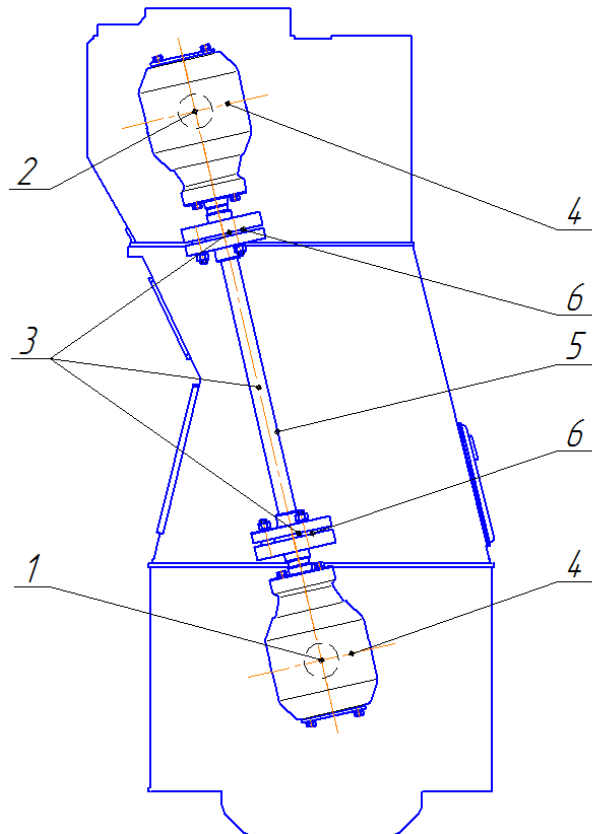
Редукторний привід розподільного валу: 1 – колінчастий вал; 2 – розподільний вал; 3 – механічний привід; 4 – конічний редуктор; 5 – проміжний вал; 6 – компенсувальна муфта
